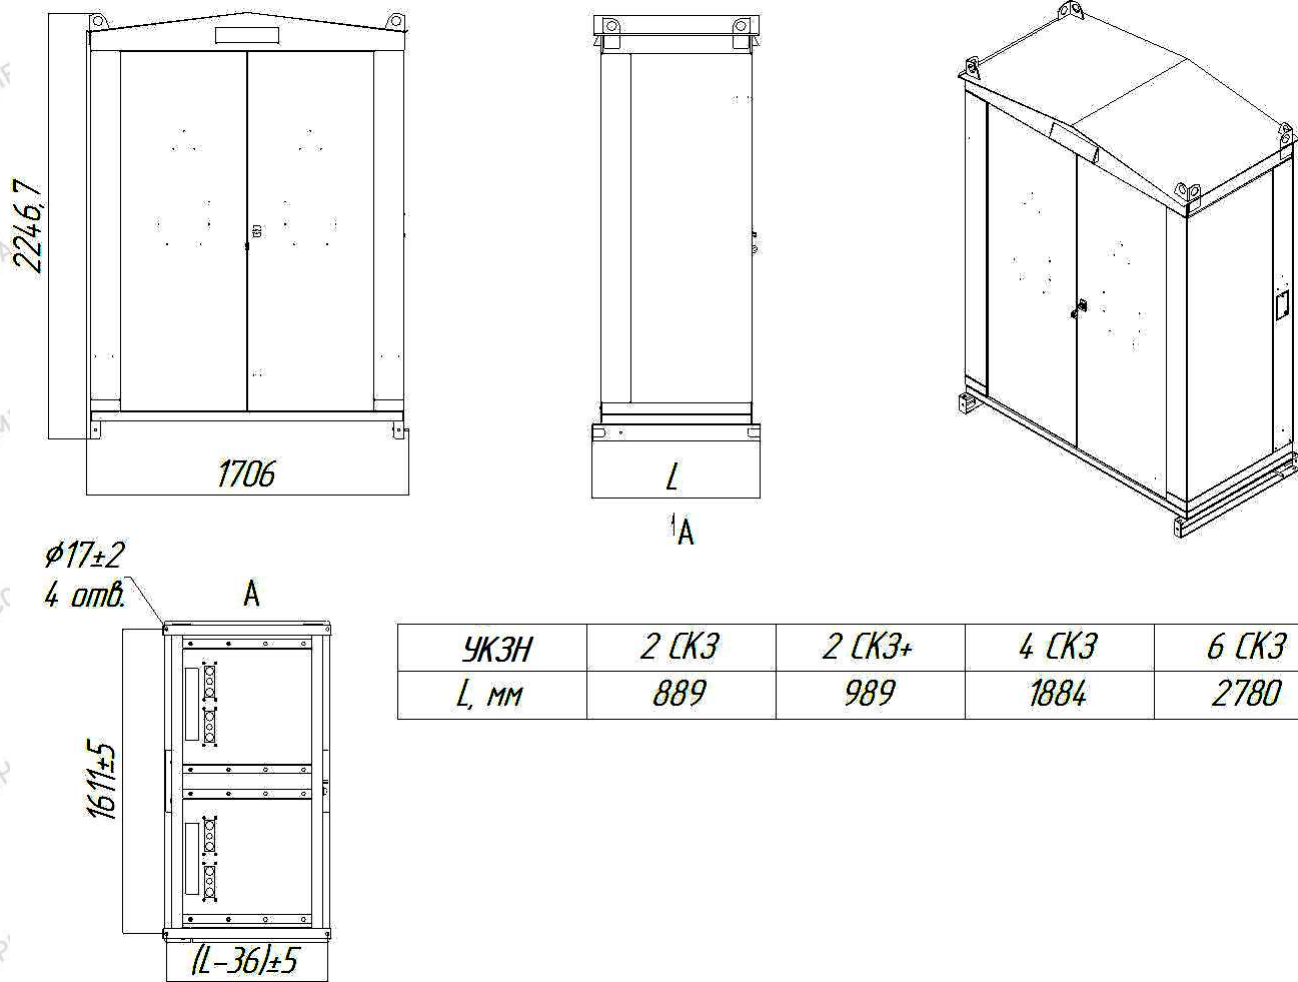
Устройство УКЗН, общий вид и габаритные размеры
